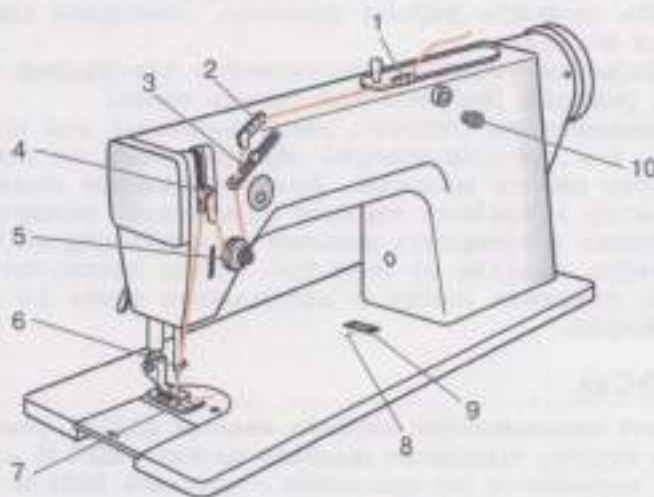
Заправка нитки и регулировка длины стежка в машине 2222-М класса: 1—3 — нитенаправители; 4 — нитеподатчик; 5 — регулятор натяжения; 6 — нитенаправитель; 7 — ушко иглы; 8 — неподвижная метка; 9 — диск; 10 — кнопка
